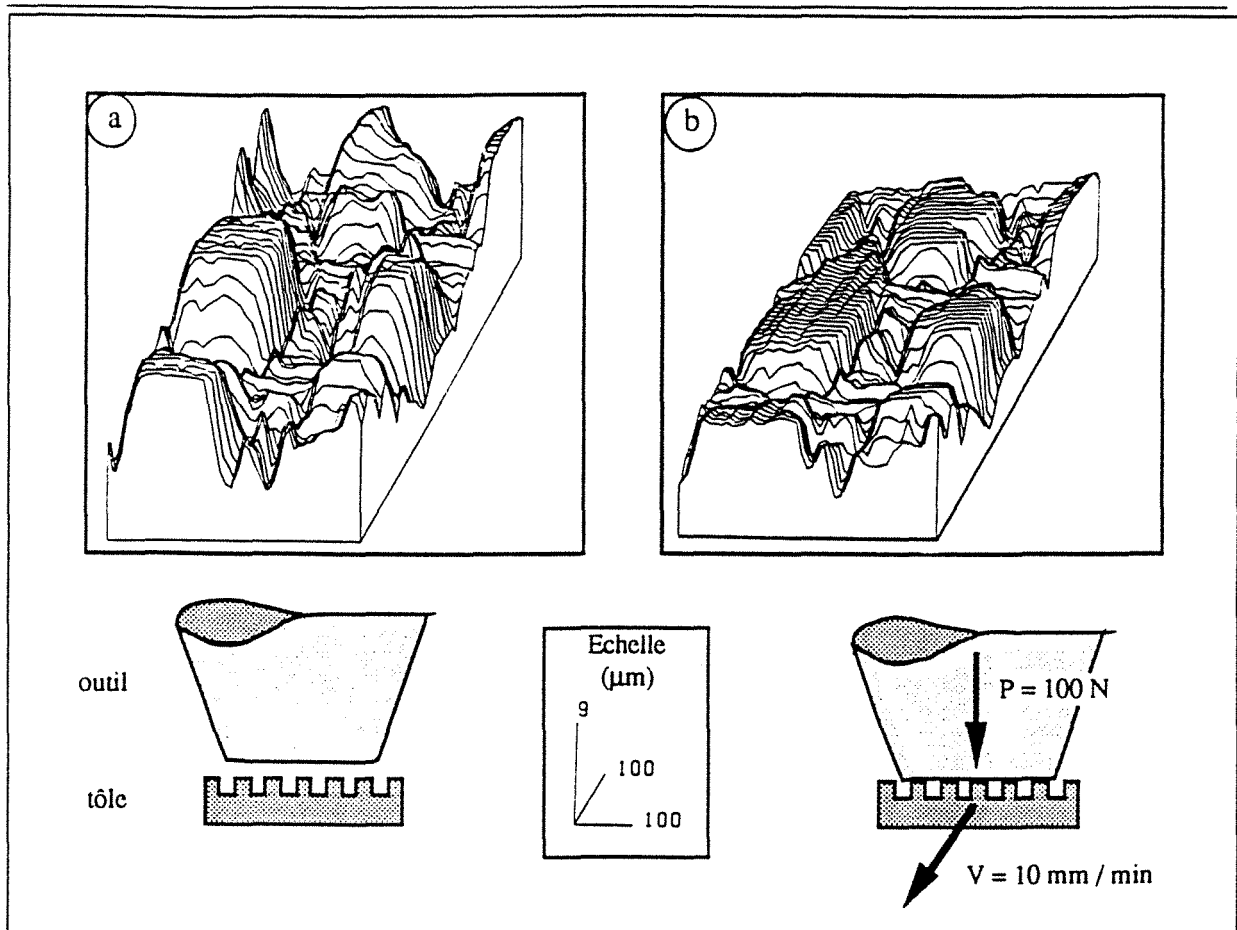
Représentations tridimensionnelles d'une même plage
